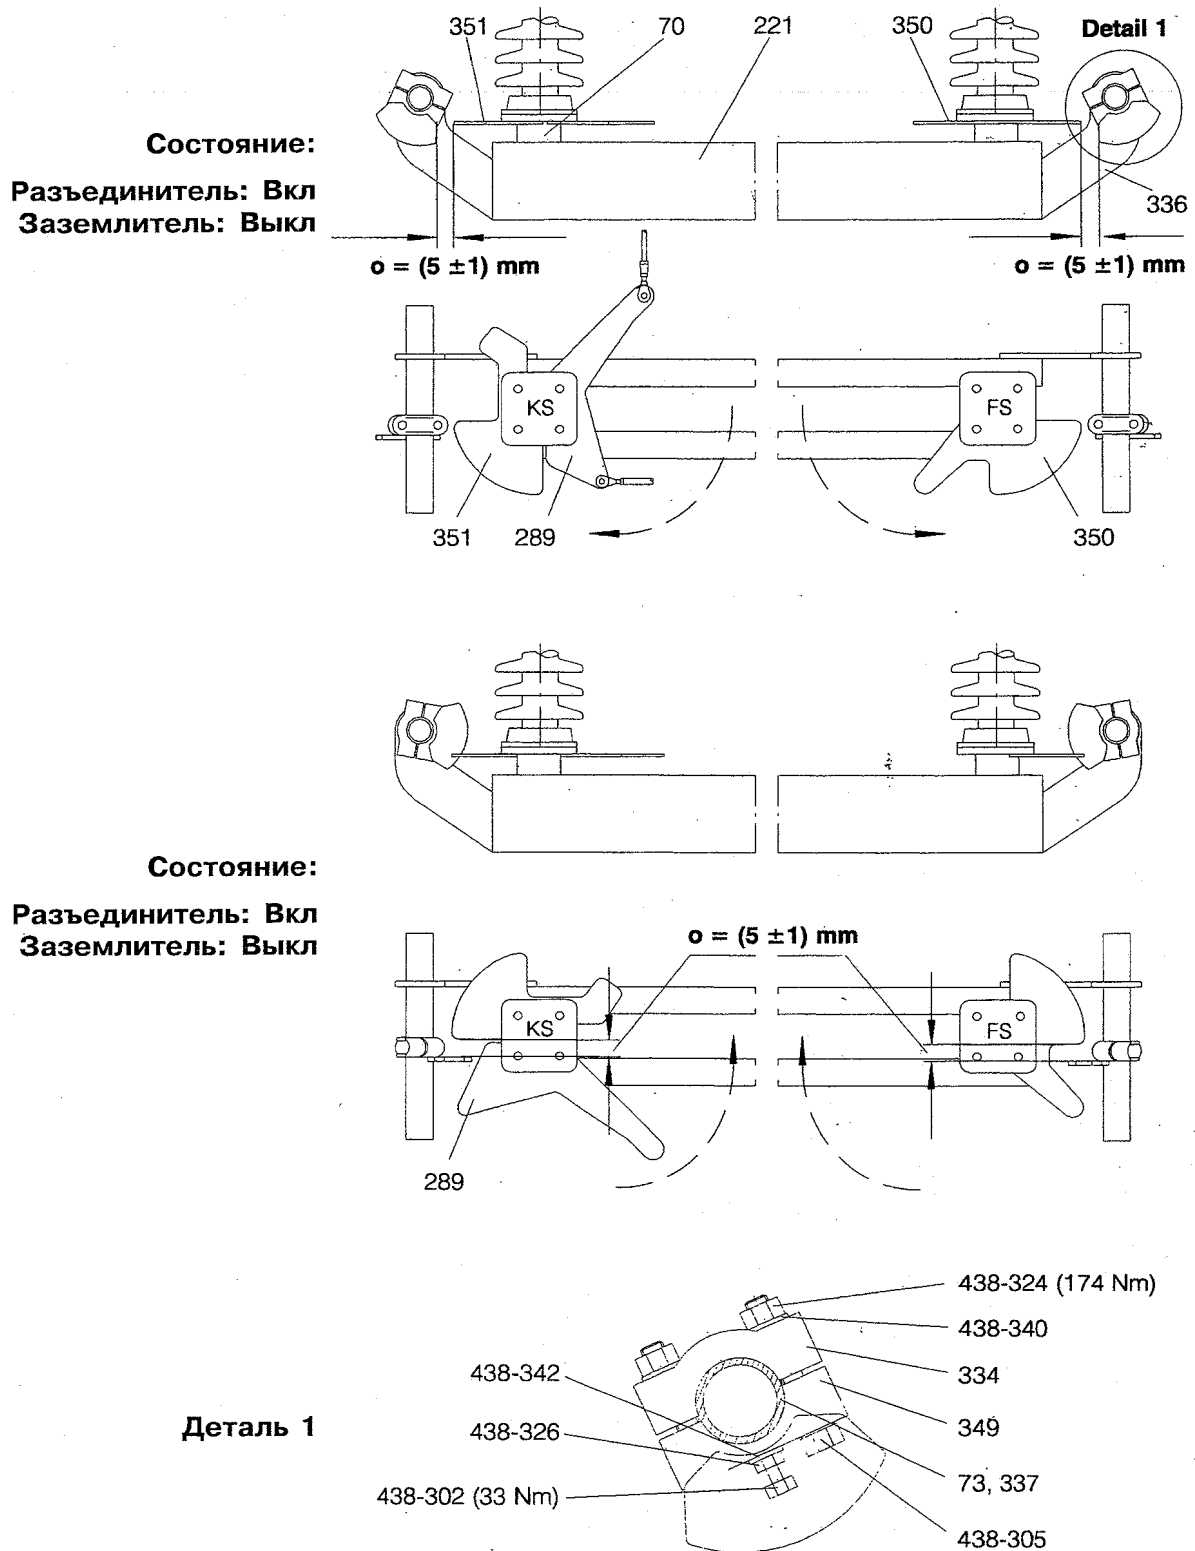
Установка змеханической блокировки. Регулировка размеров механической блокировки между разъединителем и заземлителем
